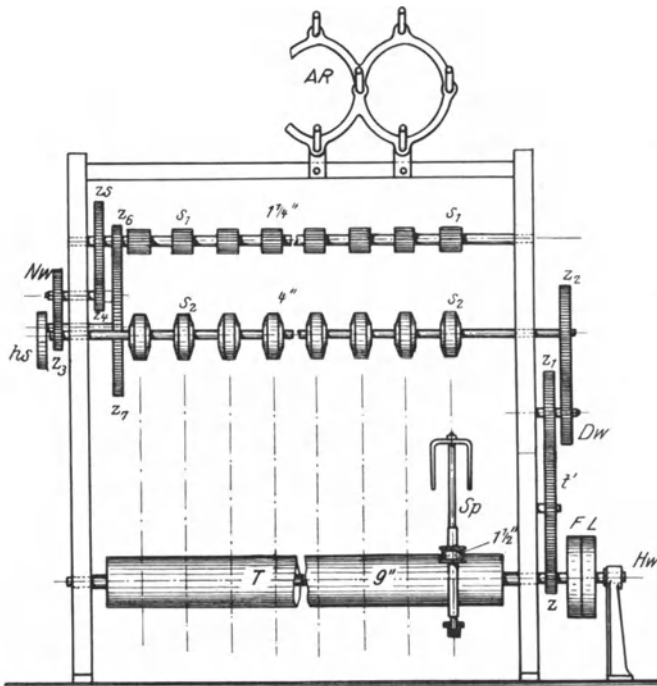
Getriebebeskizze zur Jutespinnmaschine.
